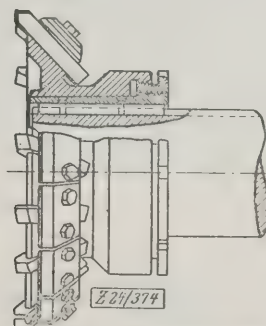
Größerer Fräskopf, auf der zylindrischen Spindel mittels kegelförmiger Klemmbüchse befestigt.
